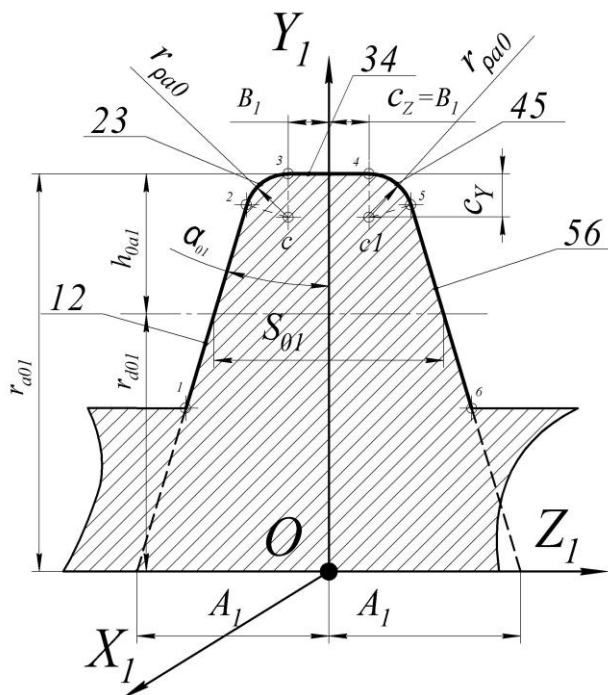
Твірний профіль вихідної інструментальної поверхні стандартної черв'ячної фрези.
